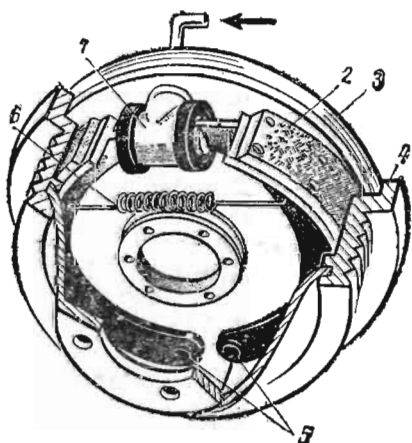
Колесный тормозной механизм с гидравлическим приводом
